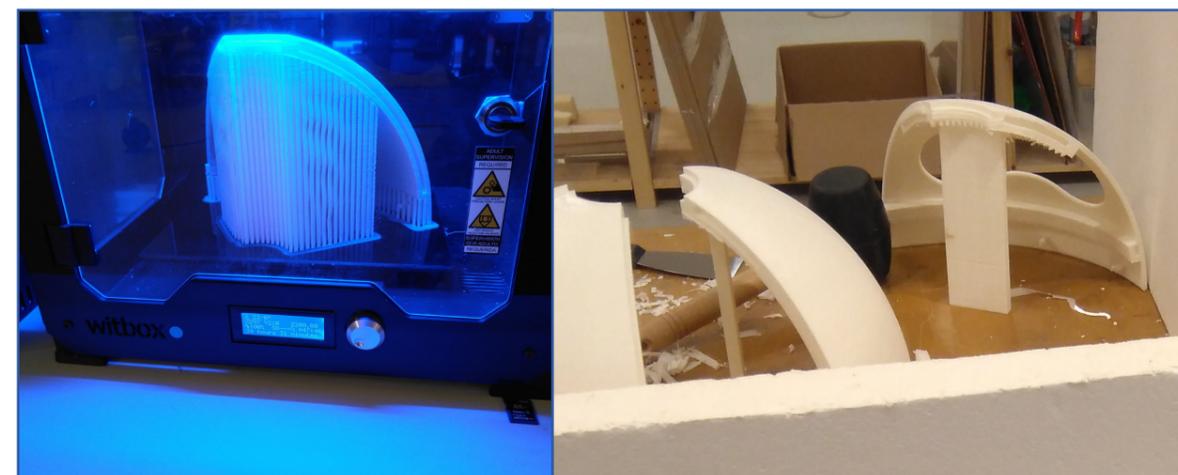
Una vez terminada la pieza, la base de impresión se situará en su posición inicial (abajo). Para extraer el pieza, abrir la tapa frontal, y sacar el plato con la pieza. Ésta se deberá retirar con una espátula (Fig. 33.).
